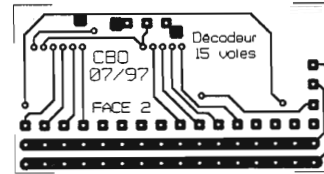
Circuit imprimé CMS, FACE 2 (dessous).
